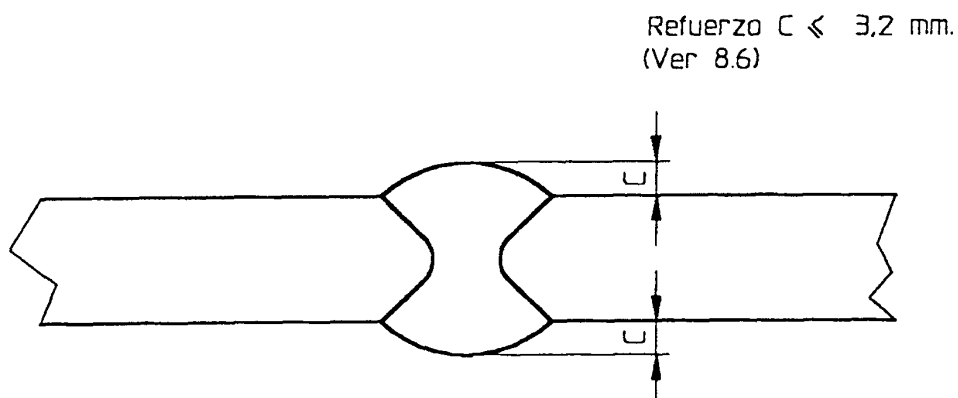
b) – Perfil de soldadura de tope aceptable
